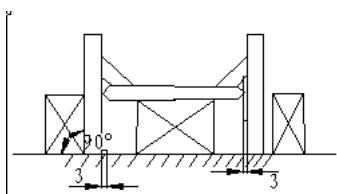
焊接 H 形钢全熔透和半熔透焊接缝坡口角度
